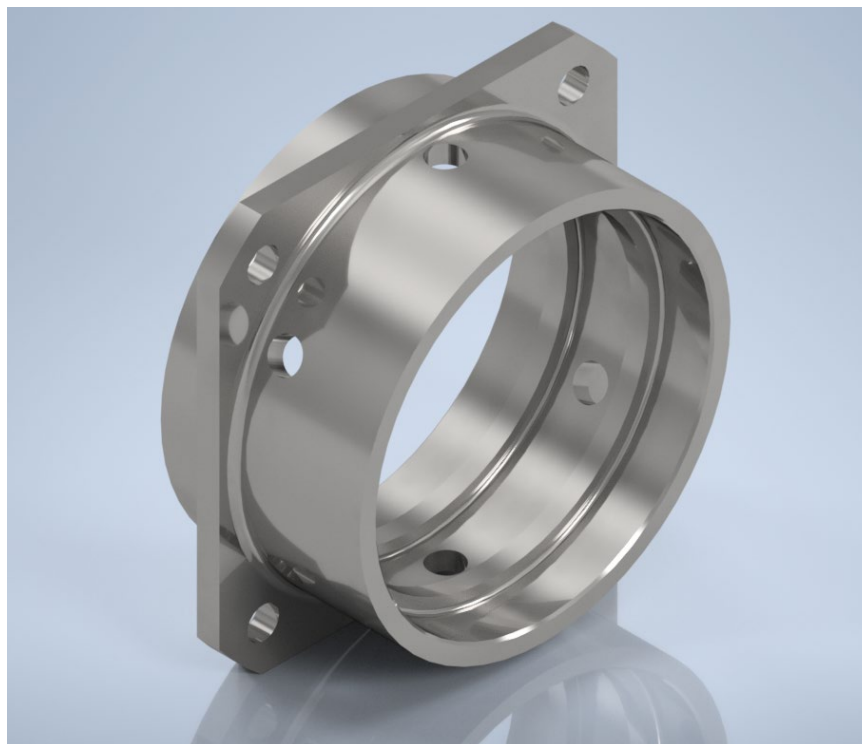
3Д модель детали «Втулка гидроцилиндра левая»
